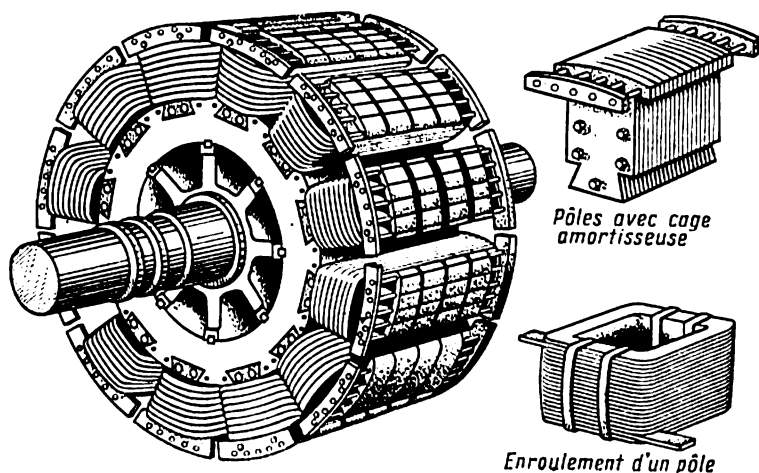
Vue extérieure d'un rotor à pôles saillants
